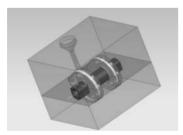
3D砂芯装配图 Fig. 4 Assembly drawing of the 3D sand core
